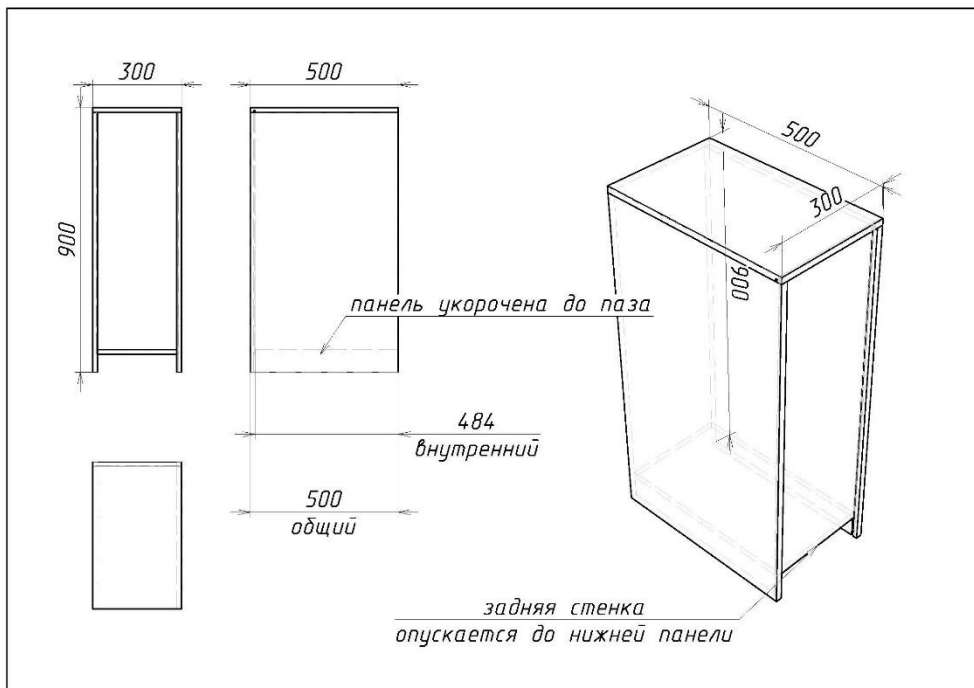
Установка задней стенки в паз в корпус с накладной крышкой и вкладным дном (БМ)
